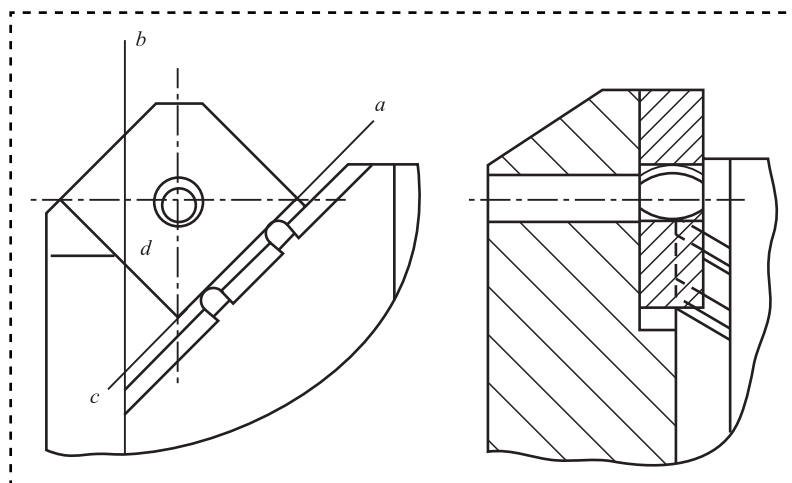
Базирование твердосплавной пластины в резцовом блоке I типа
